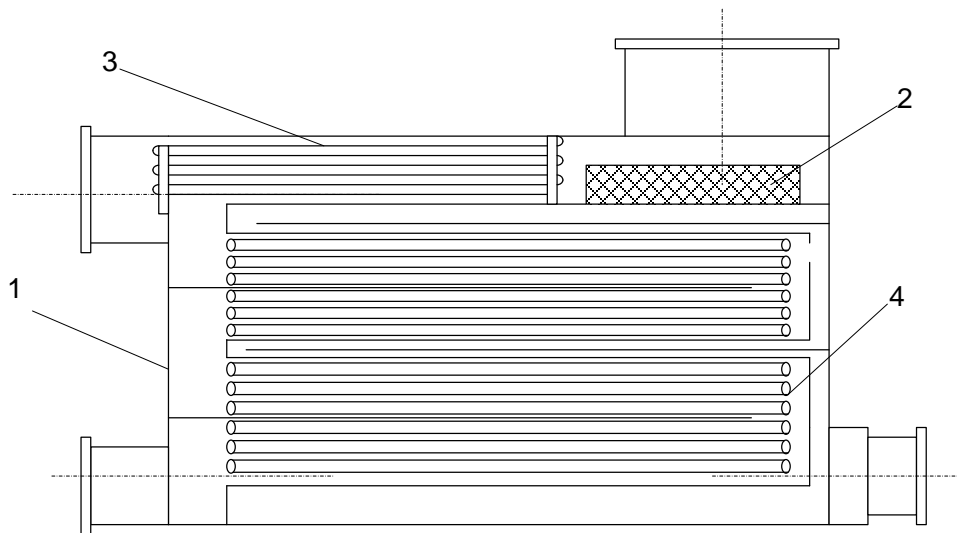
Принципова схема термokatалітичного реактора ТКРВ 0,75-0,15-0,018: 1 – корпус; 2 – електродігрівач; 3 – каталітична корзина; 4 – кожухотрубчастий рекуператор тепла
